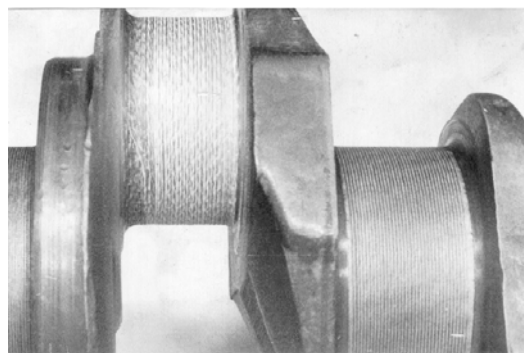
Коленчатый вал ДВС с упрочненными шатунными и коренными шейками
